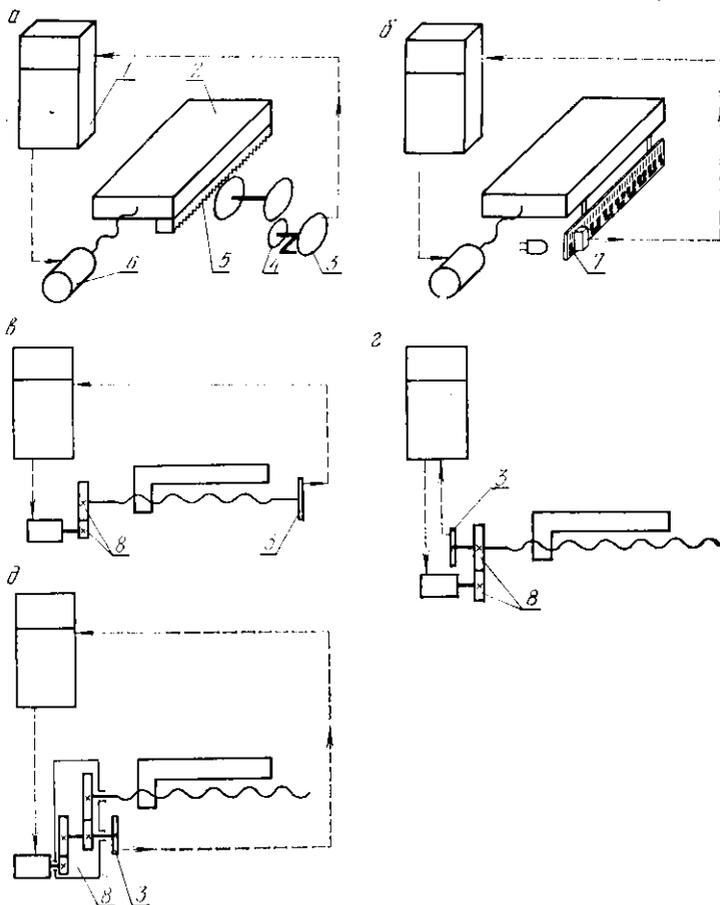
Схемы измерения перемещений в станках с ЧПУ:
